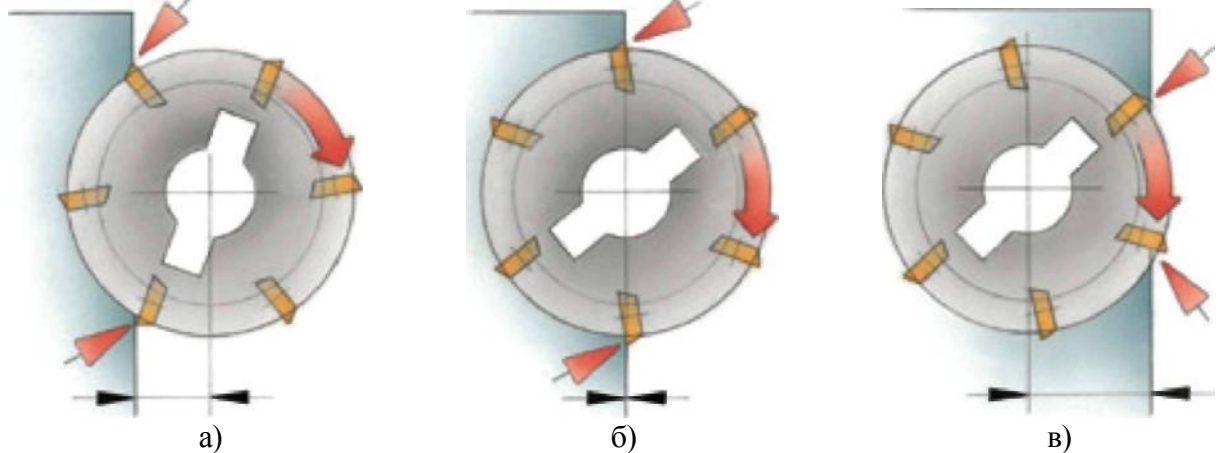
Умови врізання та виходу із зони різання зуба фрези при її різному розташуванні
